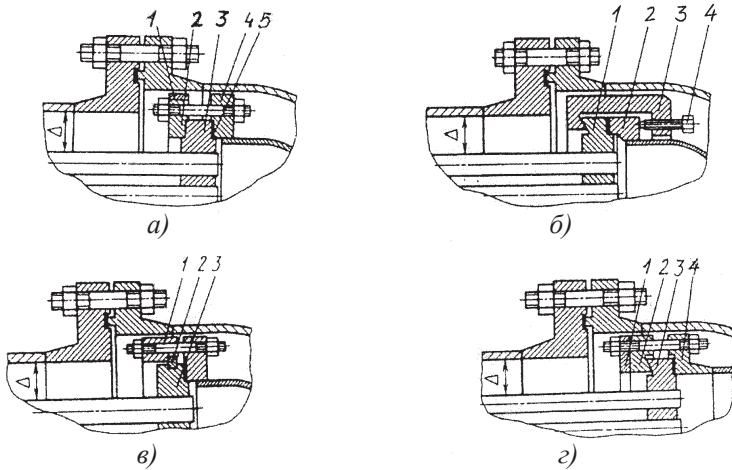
Варианты выполнения плавающей головки кожухотрубного теплообменника: *а* — разрезным фланцем: 1 — ограничительное кольцо; 2 — разрезной фланец; 3 — трубная решетка; 4 — крышка с фланцем; 5 — уплотняющая прокладка; *б* — разрезной фланцевой скобой: 1 — трубная решетка; 2 — крышка с фланцем; 3 — фланцевая скоба (два полукольца); 4 — прижимной винт; *в* — разрезным кольцом: 1 — накладной фланец; 2 — разрезное кольцо; 3 — крышка с фланцем; 4 — разрезным стяжным кольцом: 1 — накладка; 2 — разрезное кольцо; 3 — трубная решетка; 4 — крышка с фланцем
